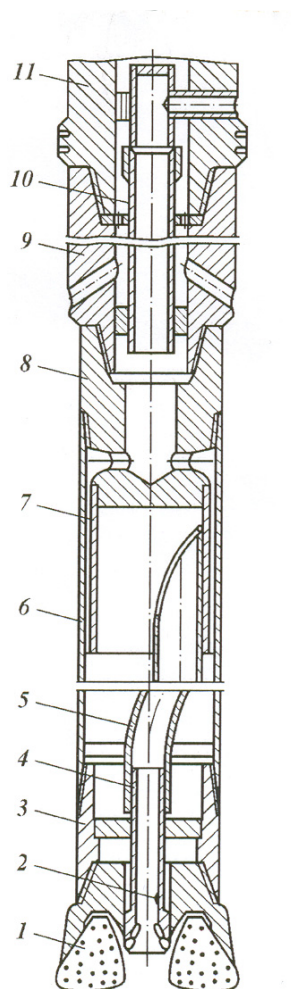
Керноотборное устройство магазинного типа серии МАГ
